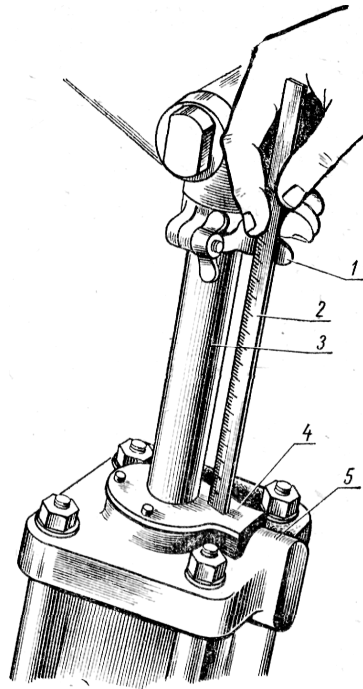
Визначення величини транспортної усадки поршня силового циліндра гідросистеми: 1 — упор; 2 — масштабна лінійка; 3 — шток; 4 — кришка чистика; 5 — силовий циліндр.
